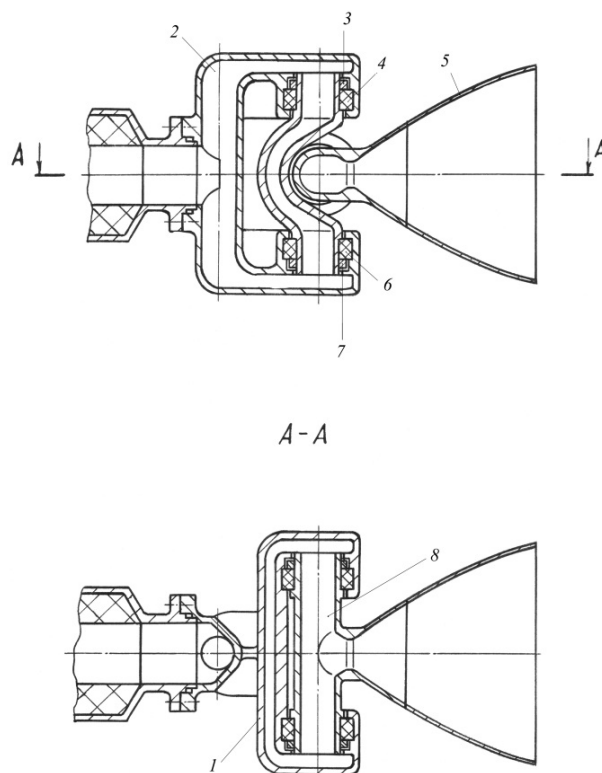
ВУС для управления в двух плоскостях: 1 – подвижная часть; 2 – неподвижная часть; 3, 7 – уплотнение; 4, 6 – подшипник; 5 – раструб; 8 – подвижный вал
